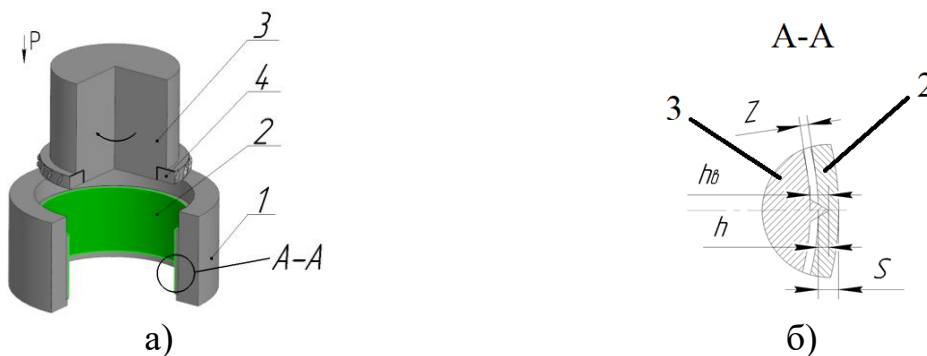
Схема процесса (а): 1 – контейнер, 2 – заготовка, 3 – инструментальный стержень, 4 – рабочая оправка; зазор между заготовкой и инструментом (б)
